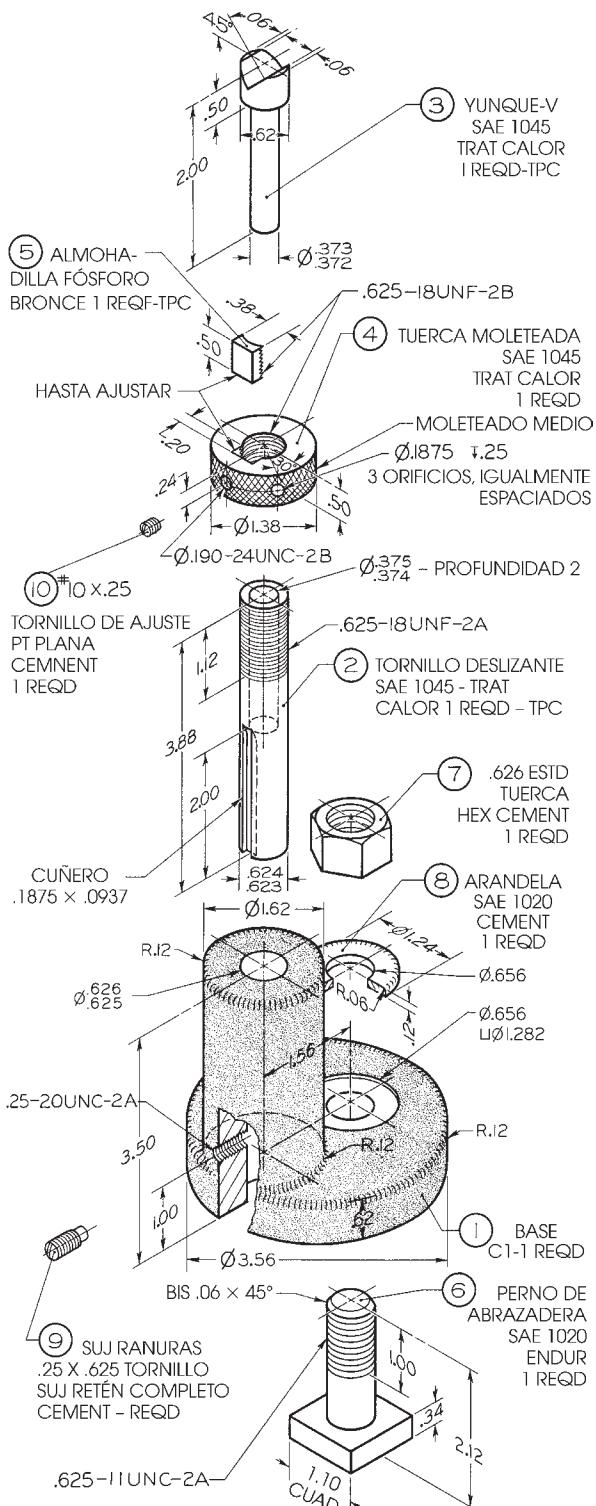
■ Gato de fresado Proy. 13.25. (1) Dibuje los detalles. (2) Dibuje el ensamble. Si así se asigna, convierta las dimensiones a unidades métricas o pulgadas decimales.
